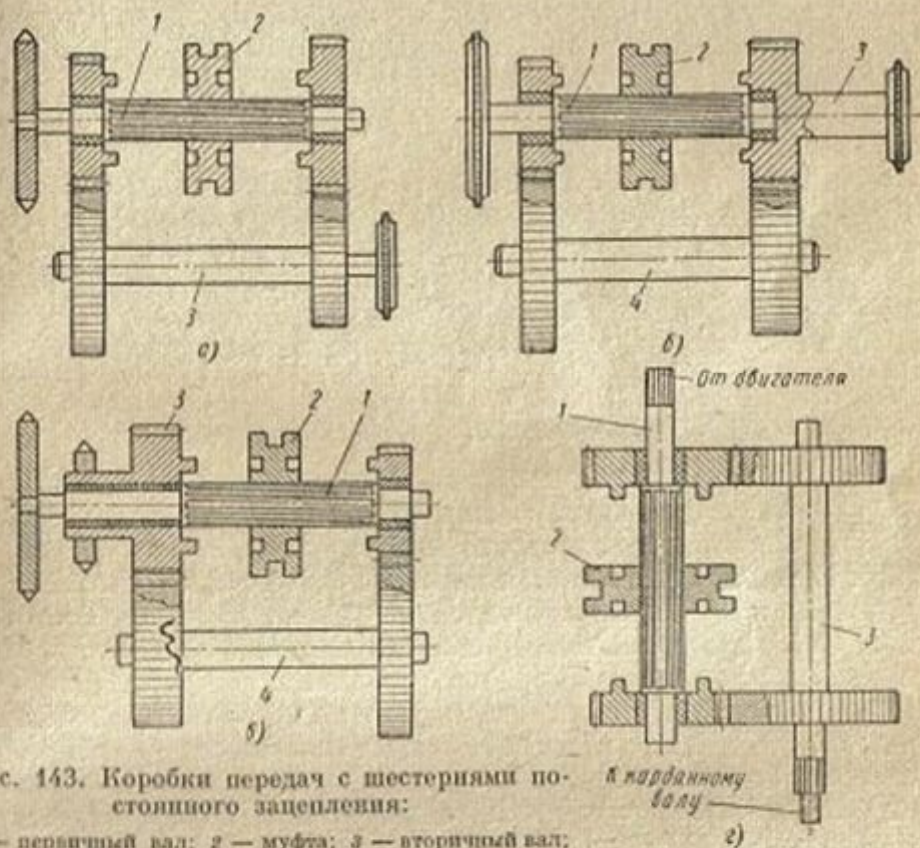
Коробки передач с шестернями постоянного зацепления:
